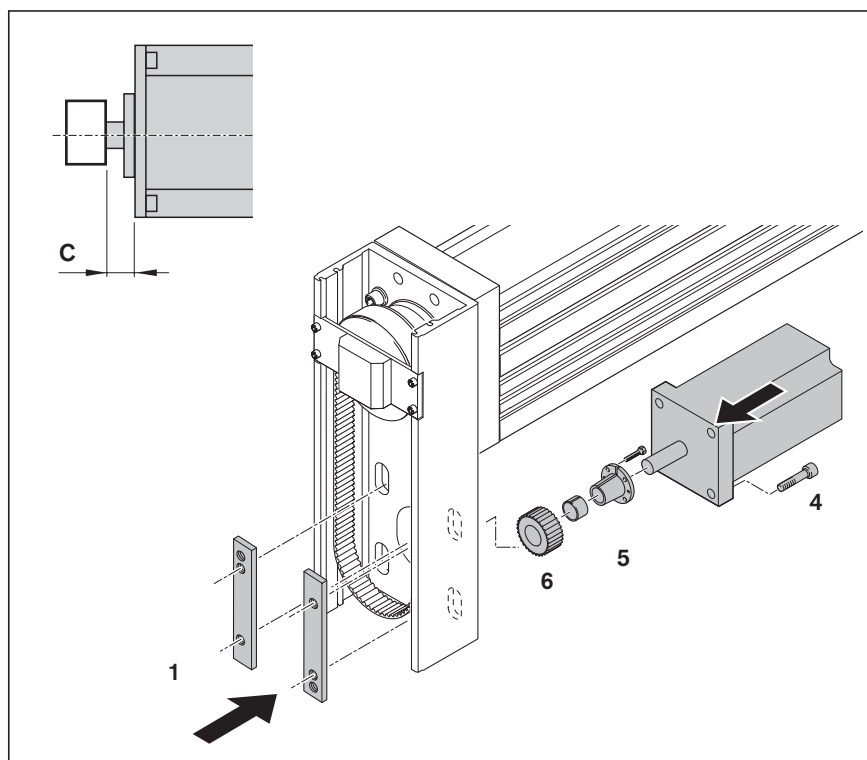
Montaje del motor y la segunda polea de la correa ($i = 1,5$ o $i = 2$)
